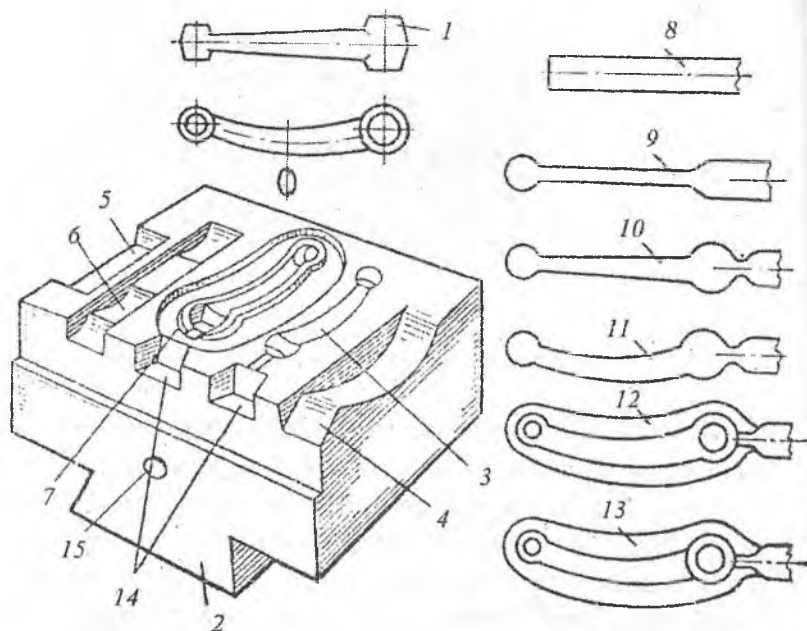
Молотовый штамп для изготовления детали "шатун":
